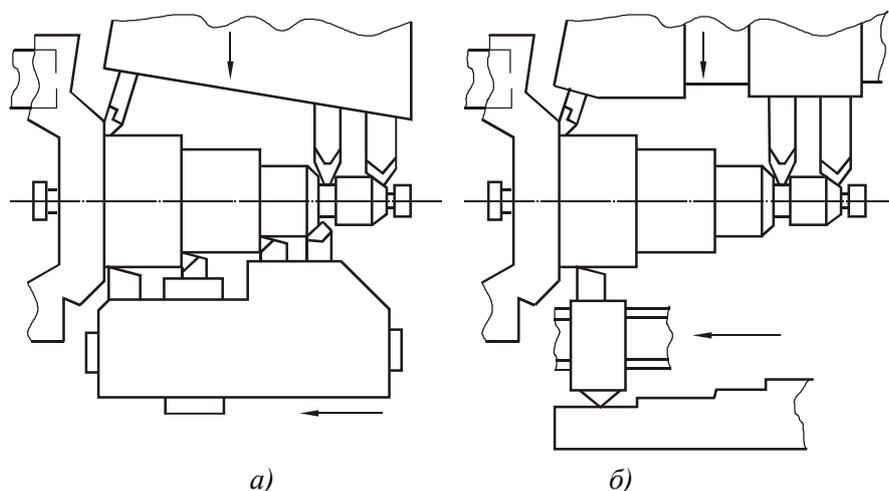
Схемы наладок многолезцовых станков: а – без копира; б – по копиру
